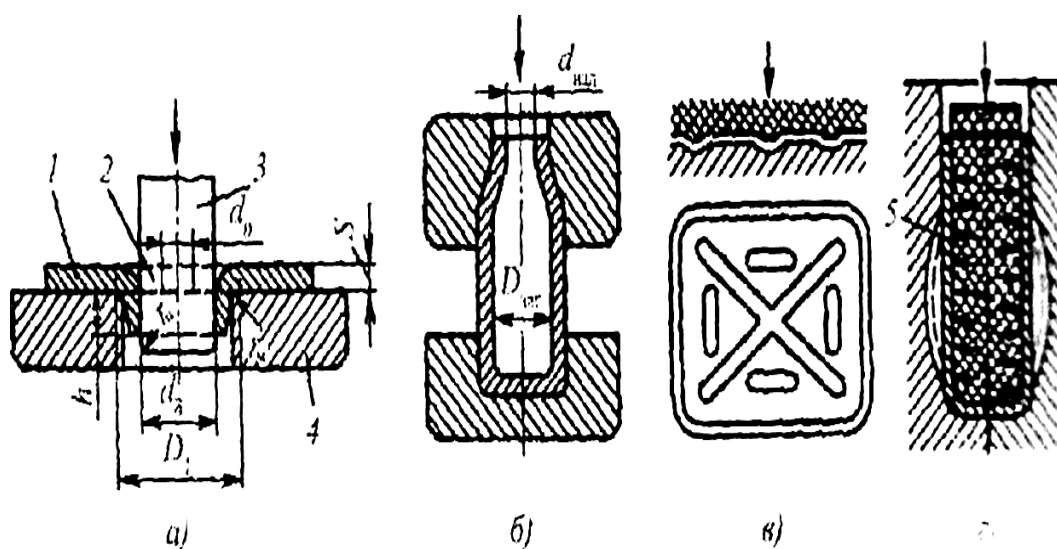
Схемы формоизменяющих операций: а - отбортовка; б - обжим; в - формовка ребер жесткости; г - формовка с раздачей; 1 - изделие; 2 - заготовка; 3 - пуансон; 4 - матрица; 5 - резиновый пуансон
